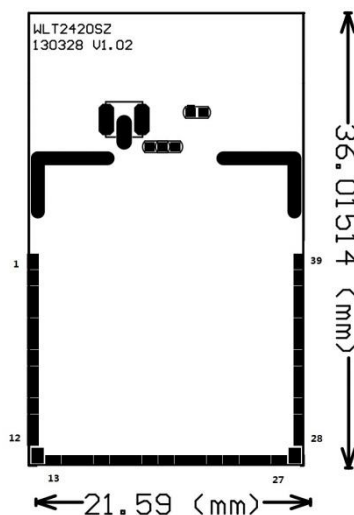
WLT2420SZ 结构尺寸【俯视图】
